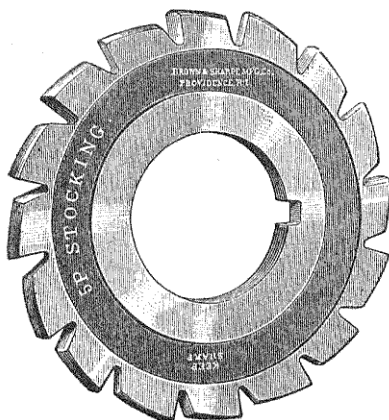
Fraise à défoncer pour la taille des engrenages.
